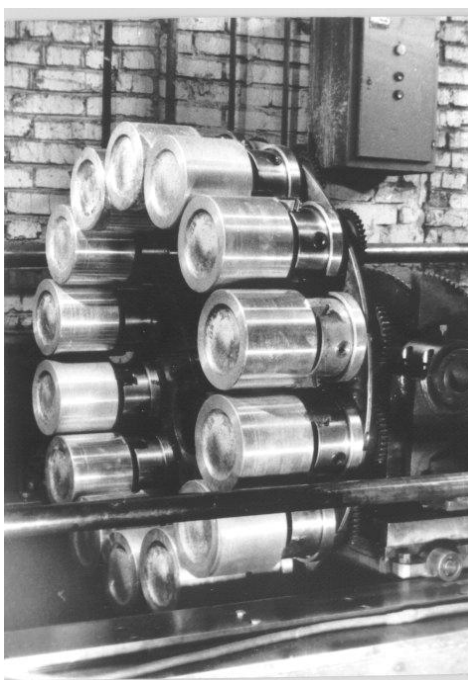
14-ти позиционный манипулятор для сварки и упрочнения поршней
